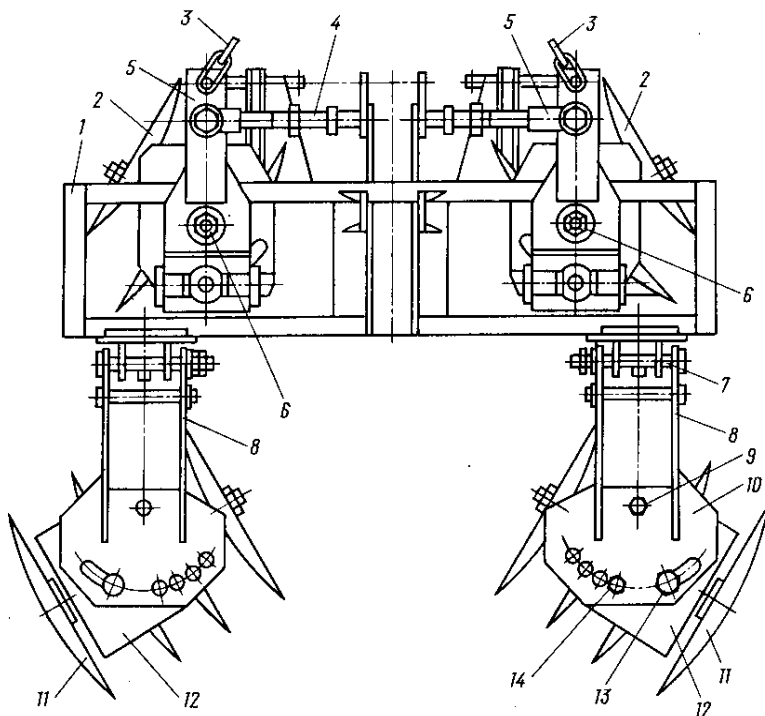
Культиватор дисковий КДС-1,8 [9]:
